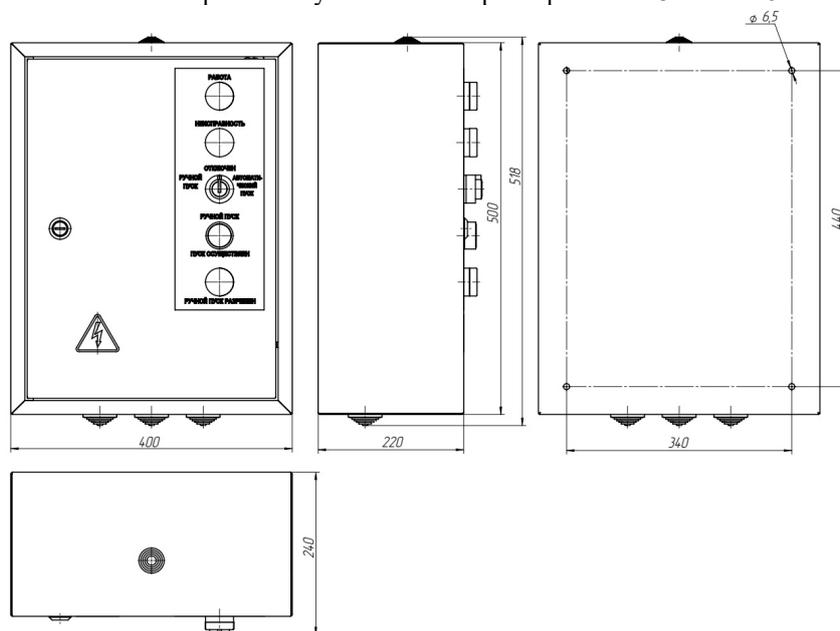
Габаритные и установочные размеры ШУП-30/ШУП-45.
